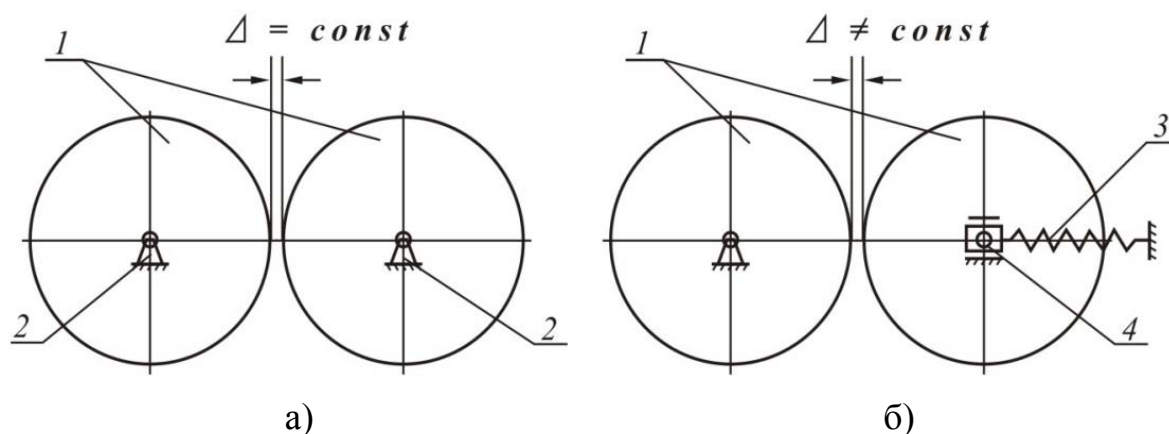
Валкові подрібнювачі: 1 - валки; 2 - нерухома опора; 3 - пружний елемент; 4 - повзун
